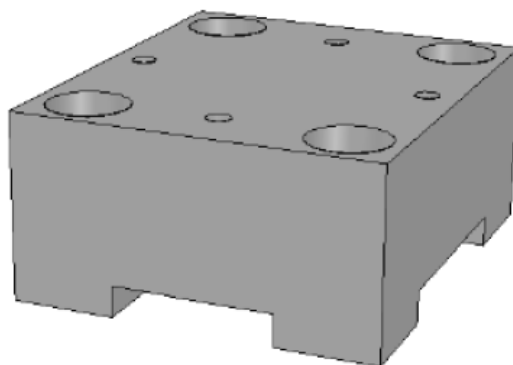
Aluminiumblock zur Befestigung des Kühlkörpers.
